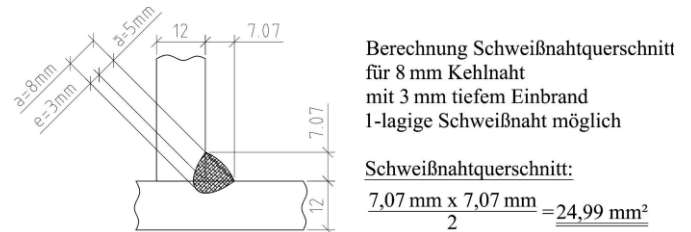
Skizze 8 mm Kehlnaht, mit 3 mm tiefem Einbrand
